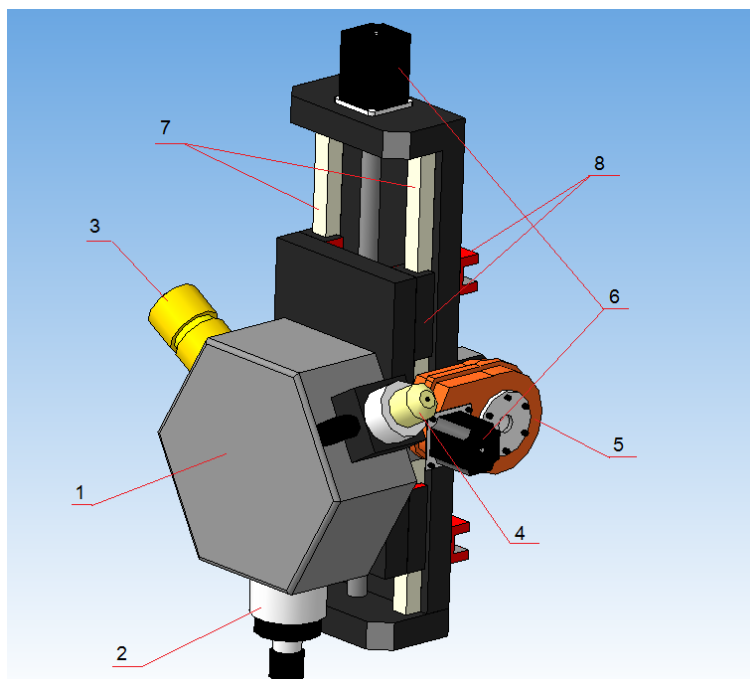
Проектная схема поворотной головки: 1 – поворотная головка; 2 – фрезерный шпиндель; 3 – плазматрон; 4 – лазерный резак; 5 – привод линейного перемещения; 6 – шаговые двигатели; 7 – рельсовые направляющие; 8 – каретки рельсовых направляющих
